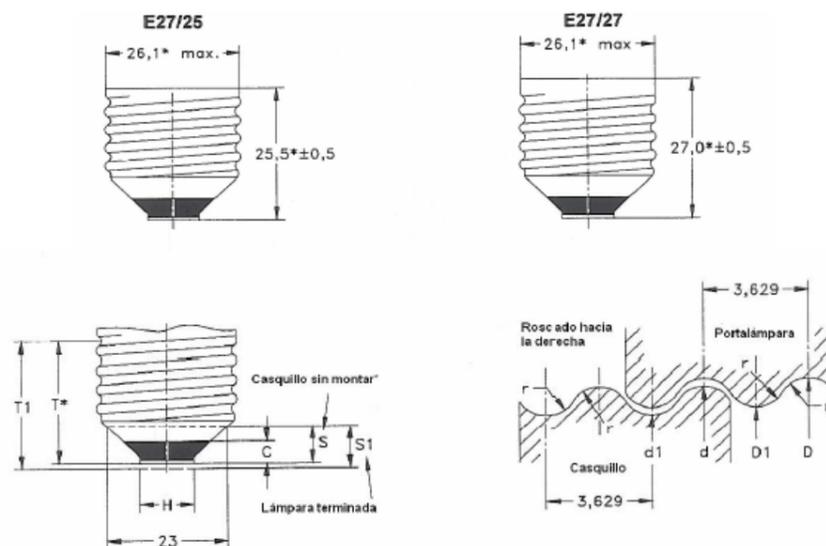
Dimensiones del casquillo de una bombilla en milímetros.
